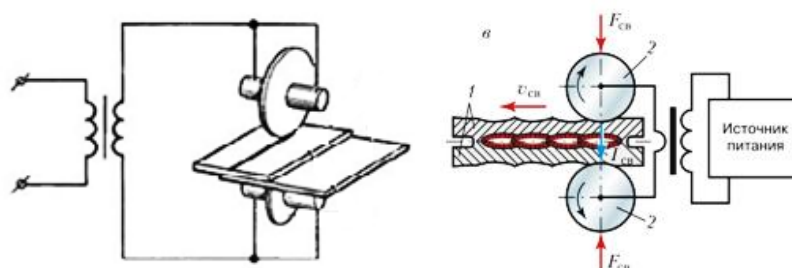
Схема шовной (роликовой) сварки
